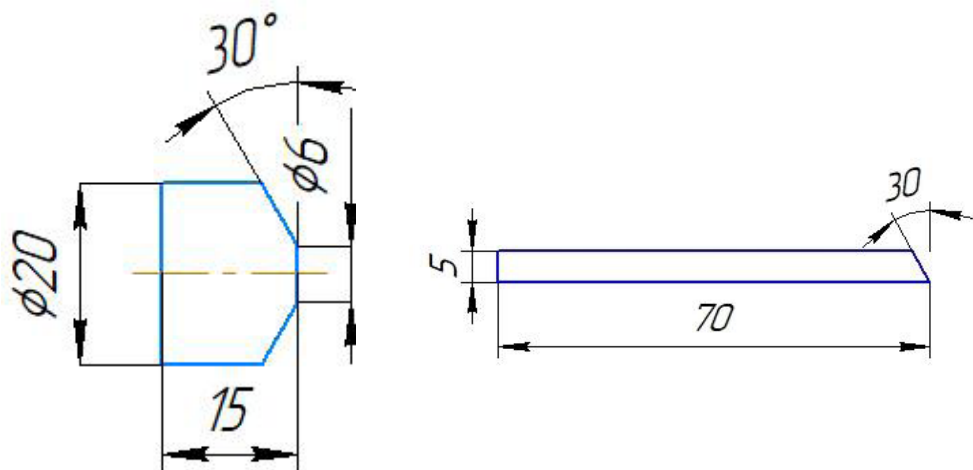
Вид сварных образцов, подготовленных под сварку методом TIG: а) цилиндрические образцы; б) пластины.
